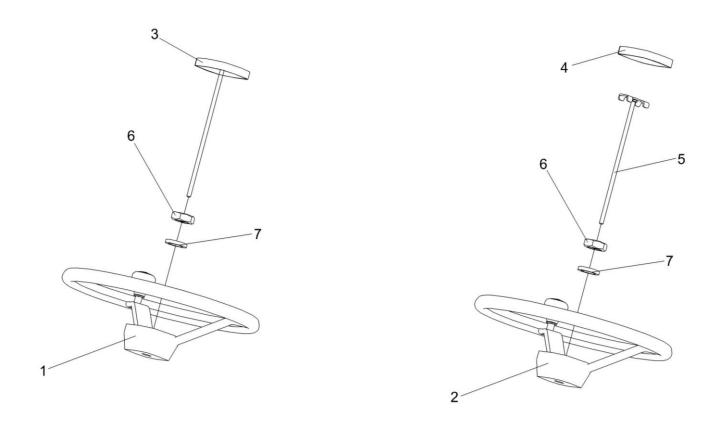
Установка колеса рулевого КЗК-12-0122600 и КЗК-12-0122600-01
